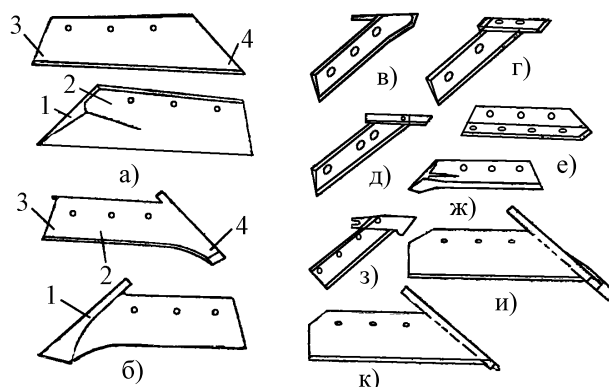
Типы лемехов: а – трапецеидальные; б – долотообразные; в – с приварной щекой; г – с накладным долотом; д – с подвижным долотом; е – со сменным лезвием; ж – самозатачивающиеся; з – со сменным долотом; и – с приварным долотом; к – с приварной планкой; 1 – магазин; 2 – лезвие; 3 – крыло; 4 – носок
